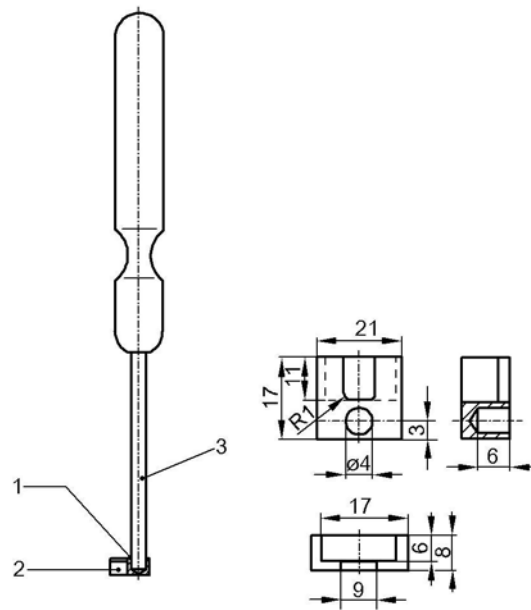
Herramienta para insertar la conexión de cable en las bobinas solenoide
